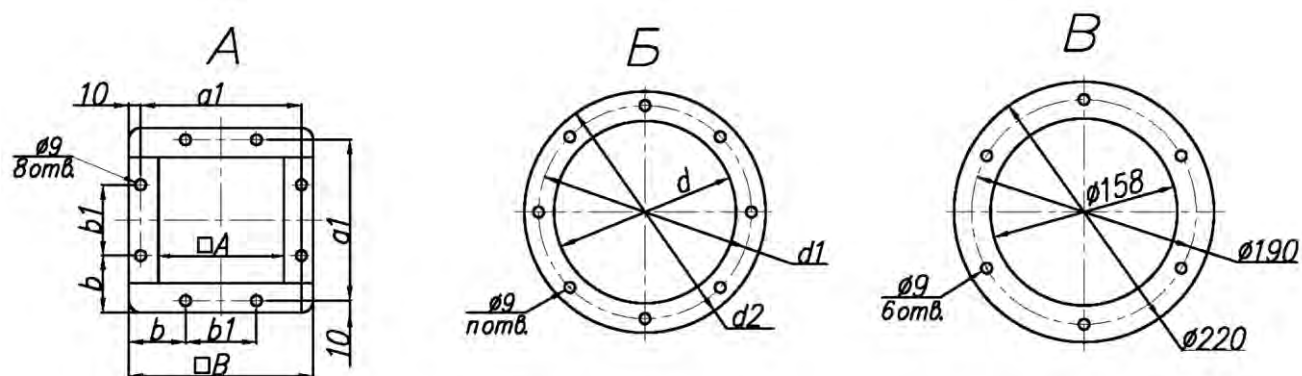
Габаритные и присоединительные размеры циклонов УЦ-38.
